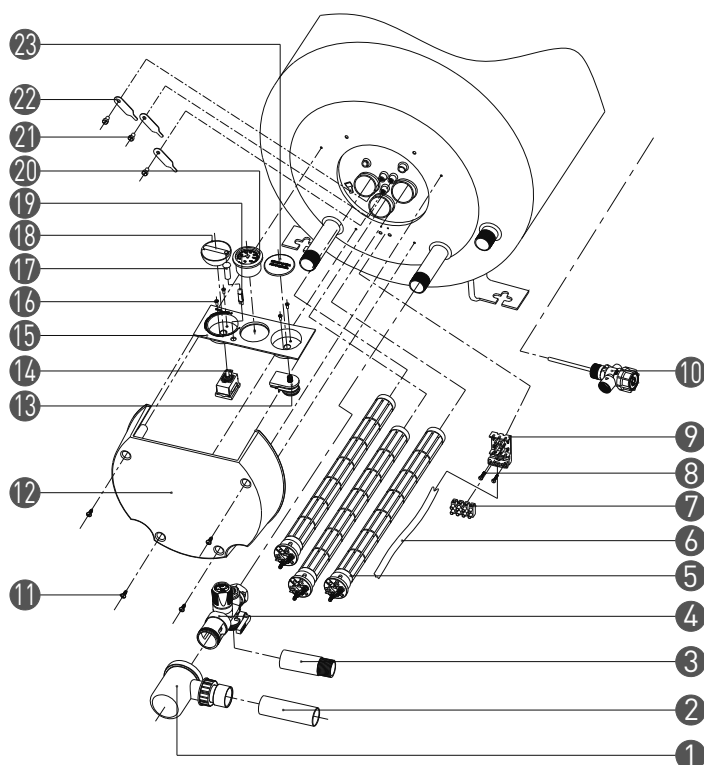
Montagem do Grupo Eléctrico e Hidráulico
